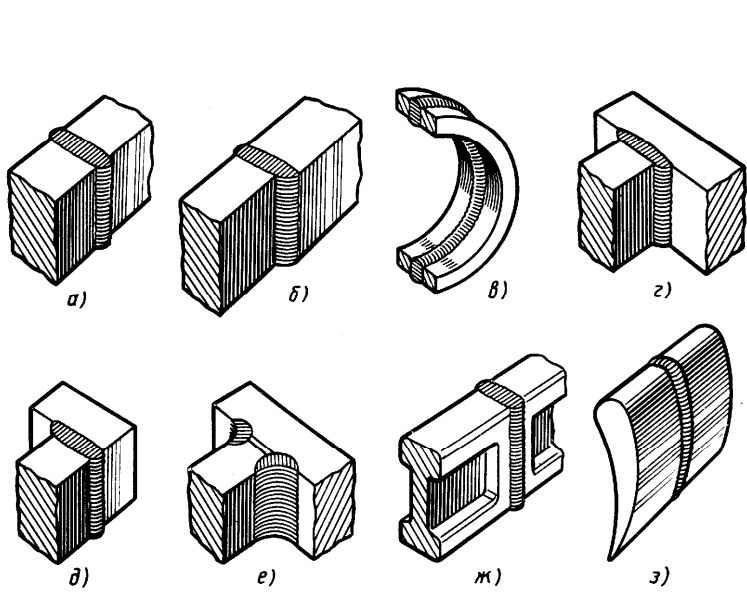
Виды сварных соединений, выполняемых электрошлаковой сваркой
